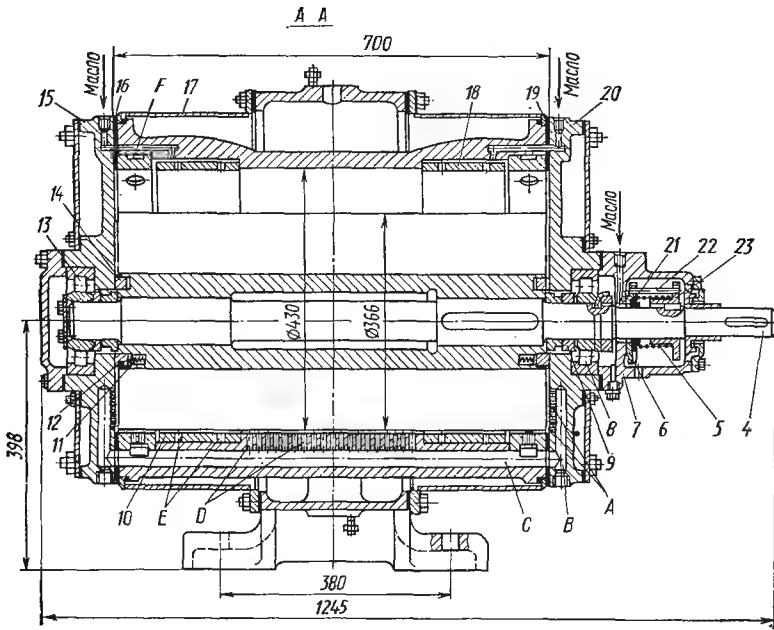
Пластинчато-роторный вакуумный насос RVN-25
